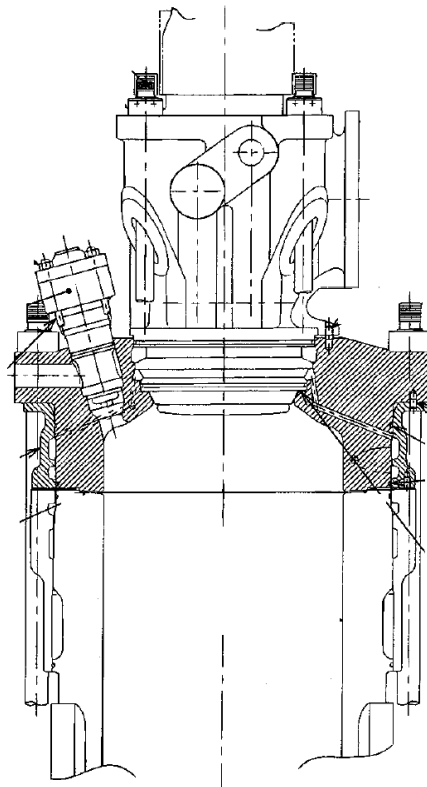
Втулка робочого циліндру двигуна 6ДКРН 80/230
